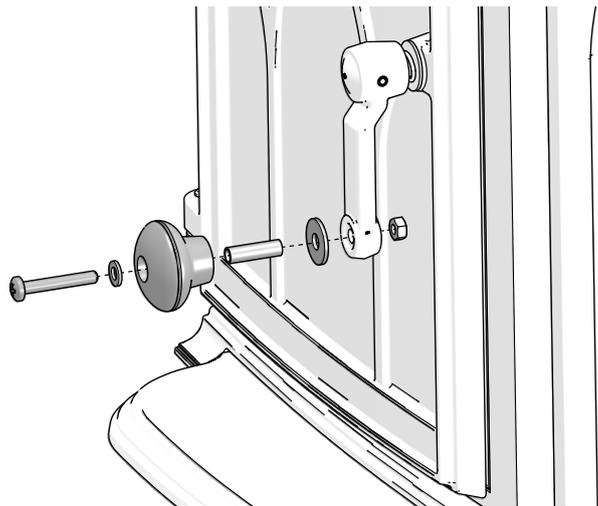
а Сборка дверной ручки для дверки зольного ящика-детали
